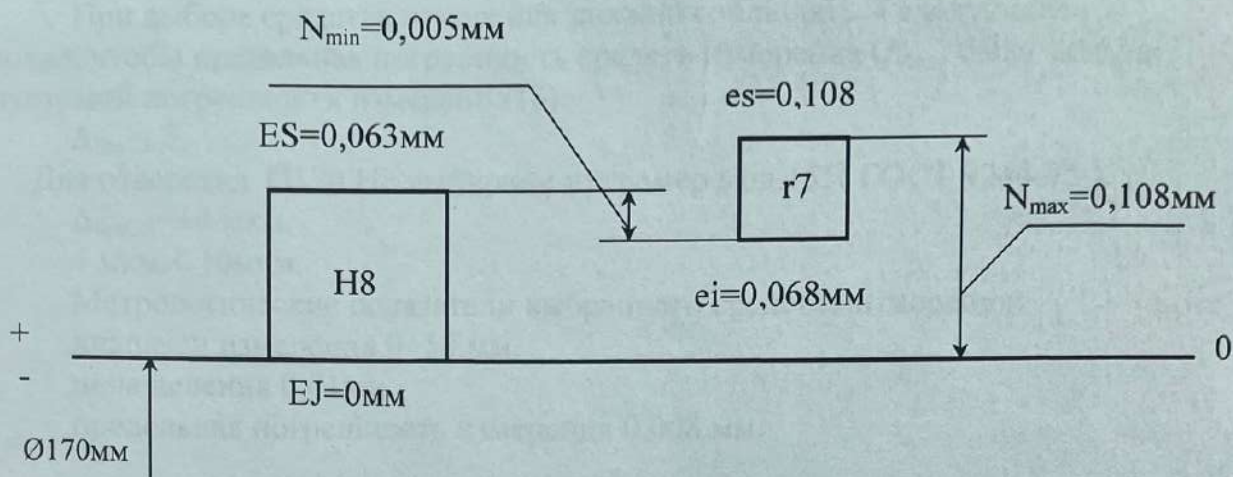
а - Схема расположения полей допусков отверстия и вала.
